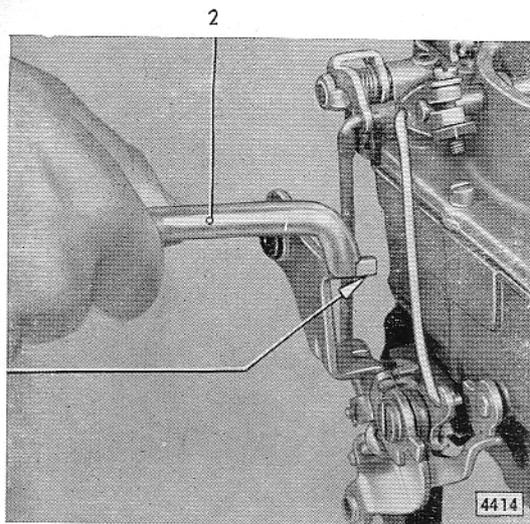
Zunge der Überlaufsicherung mit Werkzeug S-5054 nachbiegen
